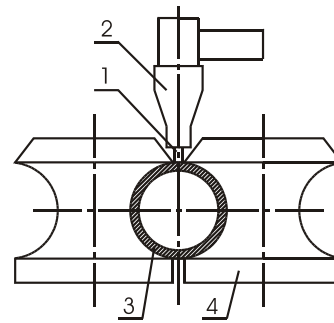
Схема аргоно-дуговой сварки труб:
